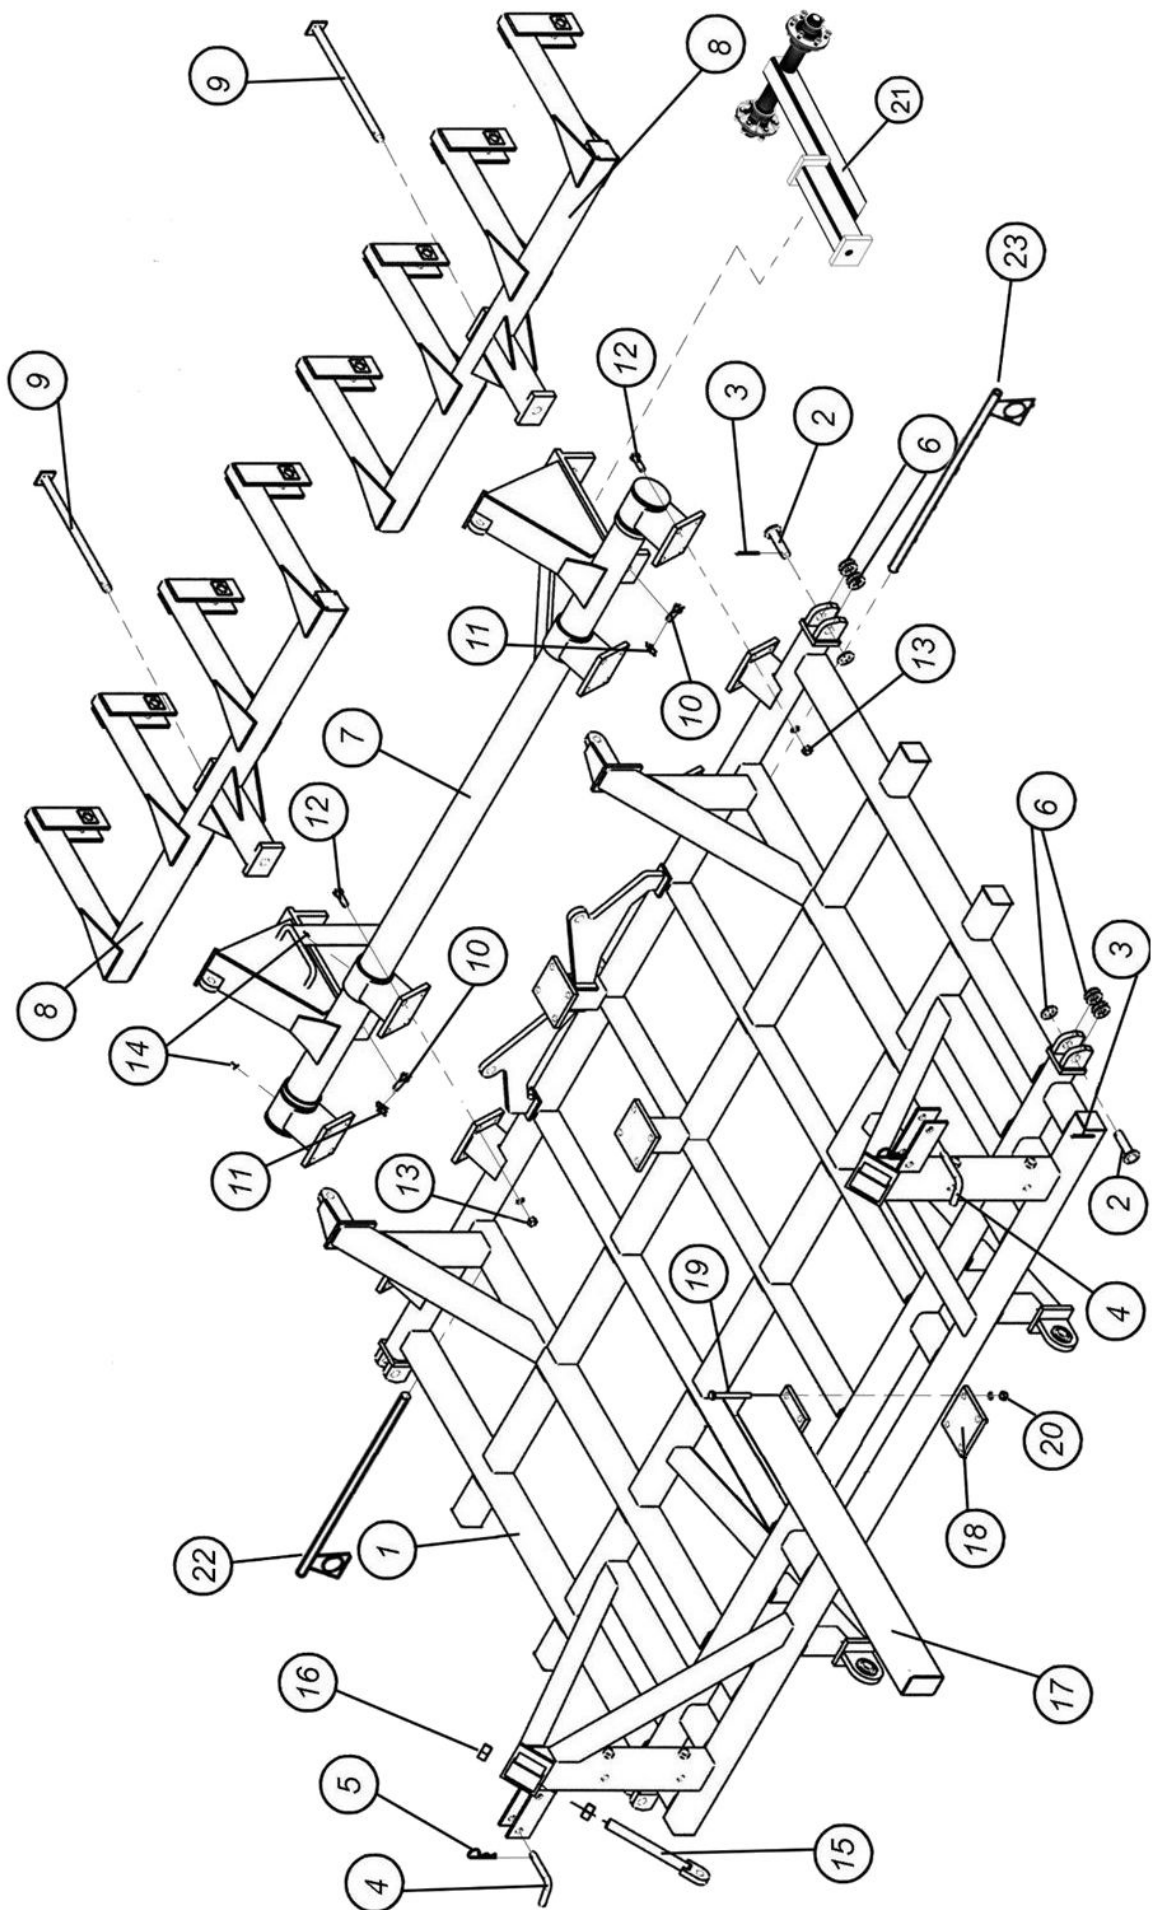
Главная рама с узлом качающегося вала и подвеской прикатывающих колес
